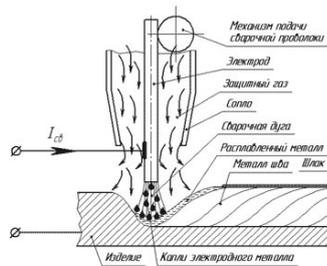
Схема сварки в защитных газах
